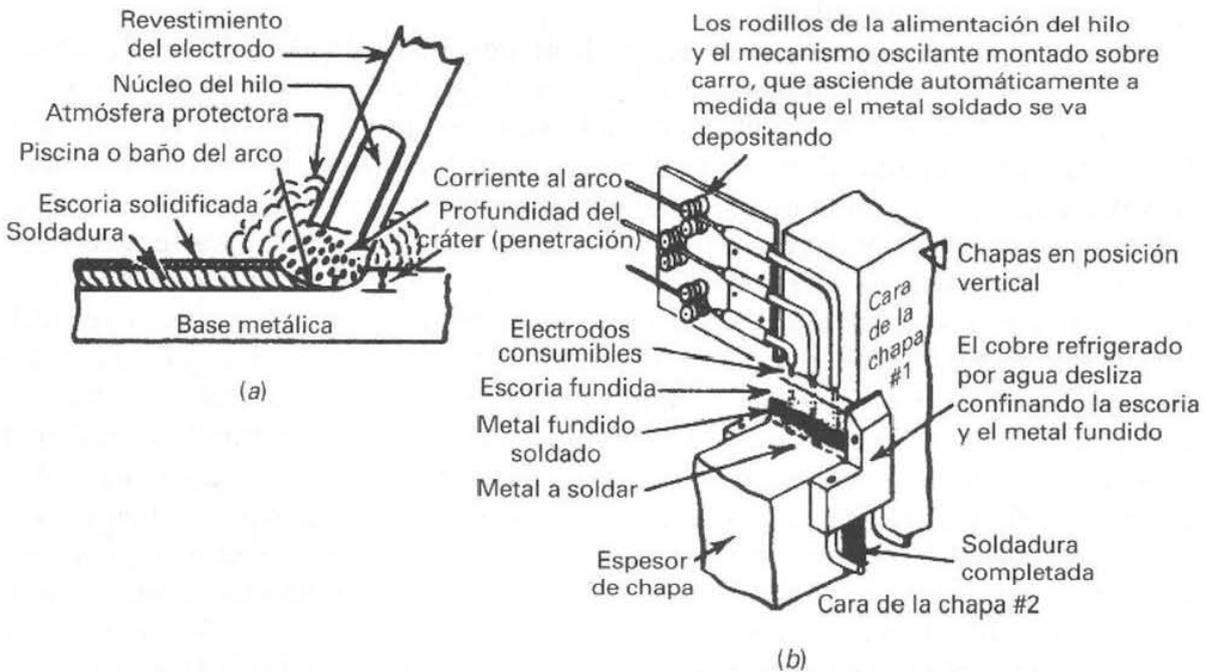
(a) Soldadura metálica de arco. (b) Elementos básicos de la electro-soldadura con escoria.
